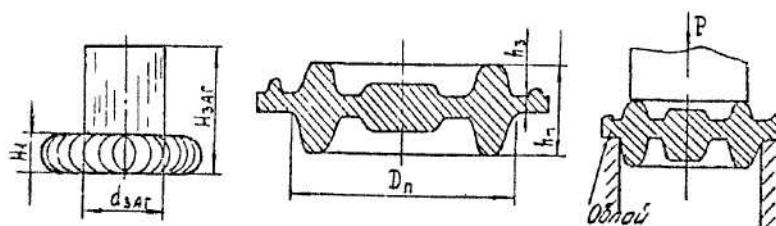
Технологические переходы получения поковки шестерни: а) предварительная осадка; б) штамповка; в) обрезка облоя
